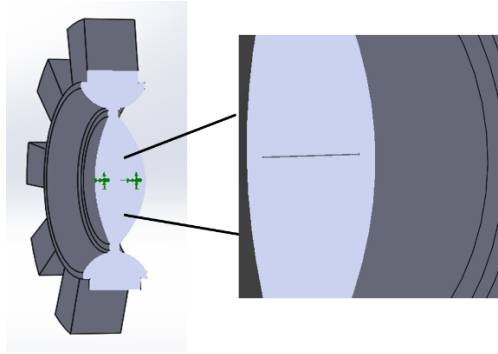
Vista de sección lateral de la pieza donde se muestra la geometría fija aplicada y la cavidad creada.
